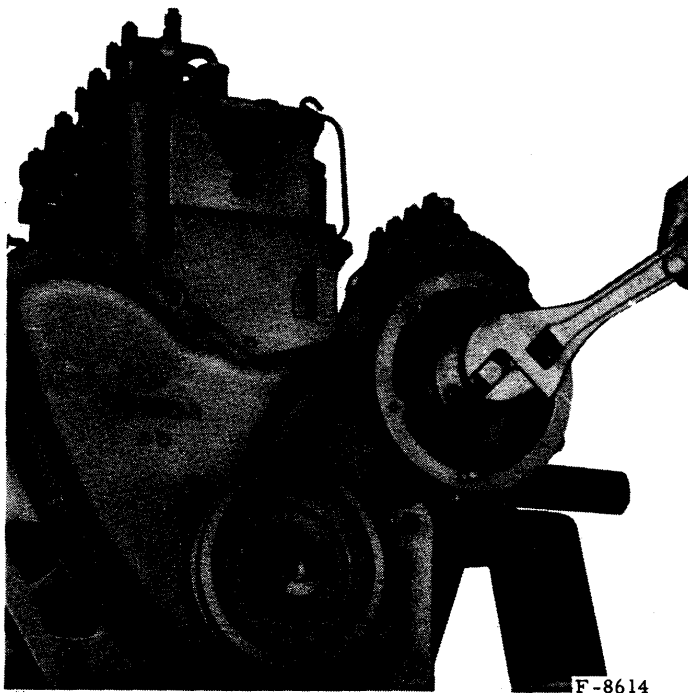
Emploi de l'arrache-moyeu pour décoller le moyeu d'accouplement de la pompe d'injection
